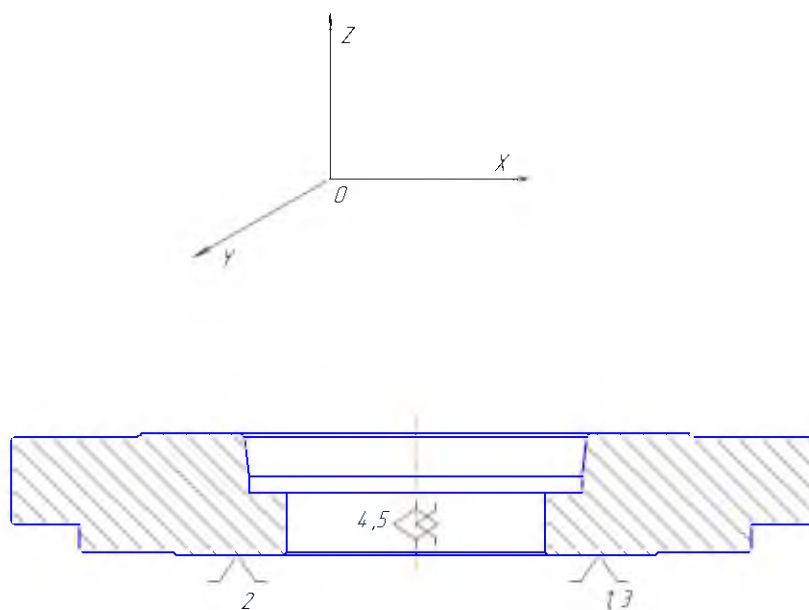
Схема базування при токарній обробці лівого торця фланця, внутрішнього кінцевого отвору та зовнішньої циліндричної поверхні
